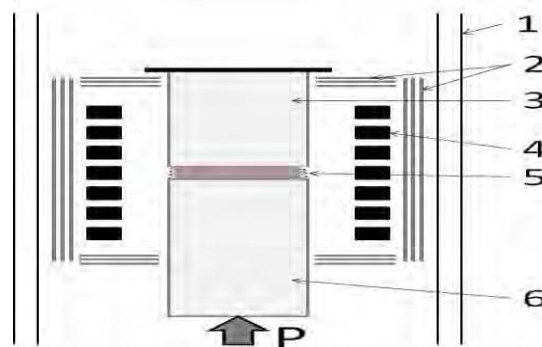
Основные узлы установки для диффузионной сварки: 1 – корпус, охлаждаемый водой, 2 – система тепловых экранов из графитовой прессованной ваты, 3 – неподвижный пуансон, 4 – нагреватель из высокопрочного графита, 5 – многослойный пакет, 6 – подвижный пуансон
